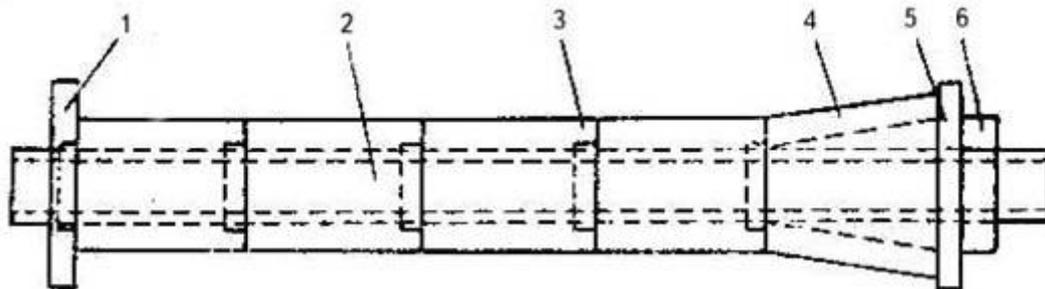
Наборка центровых трубок и воронки: 1 – шайба для нижней трубки; 2 – металлическая труба (основная); 3 – шамотная трубка; 4 – воронка; 5 – закрепляющая шайба; 6 – гайка
